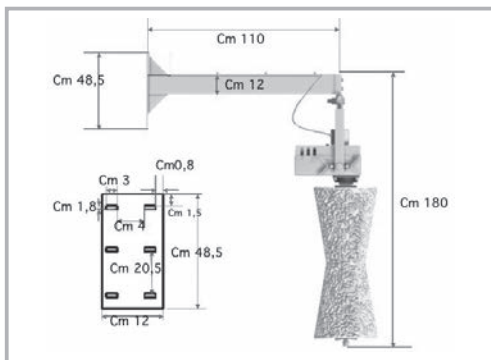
CowCleaner Swing : Montiert mit Installationsmaßen
